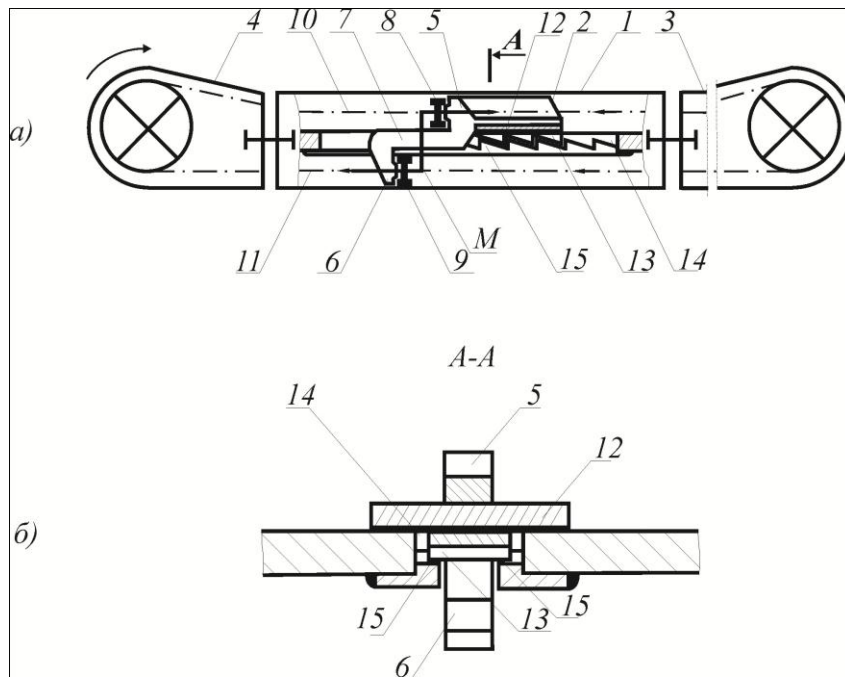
Схема стопорно-фіксуєчого пристрою скребоквого конвеєра:
